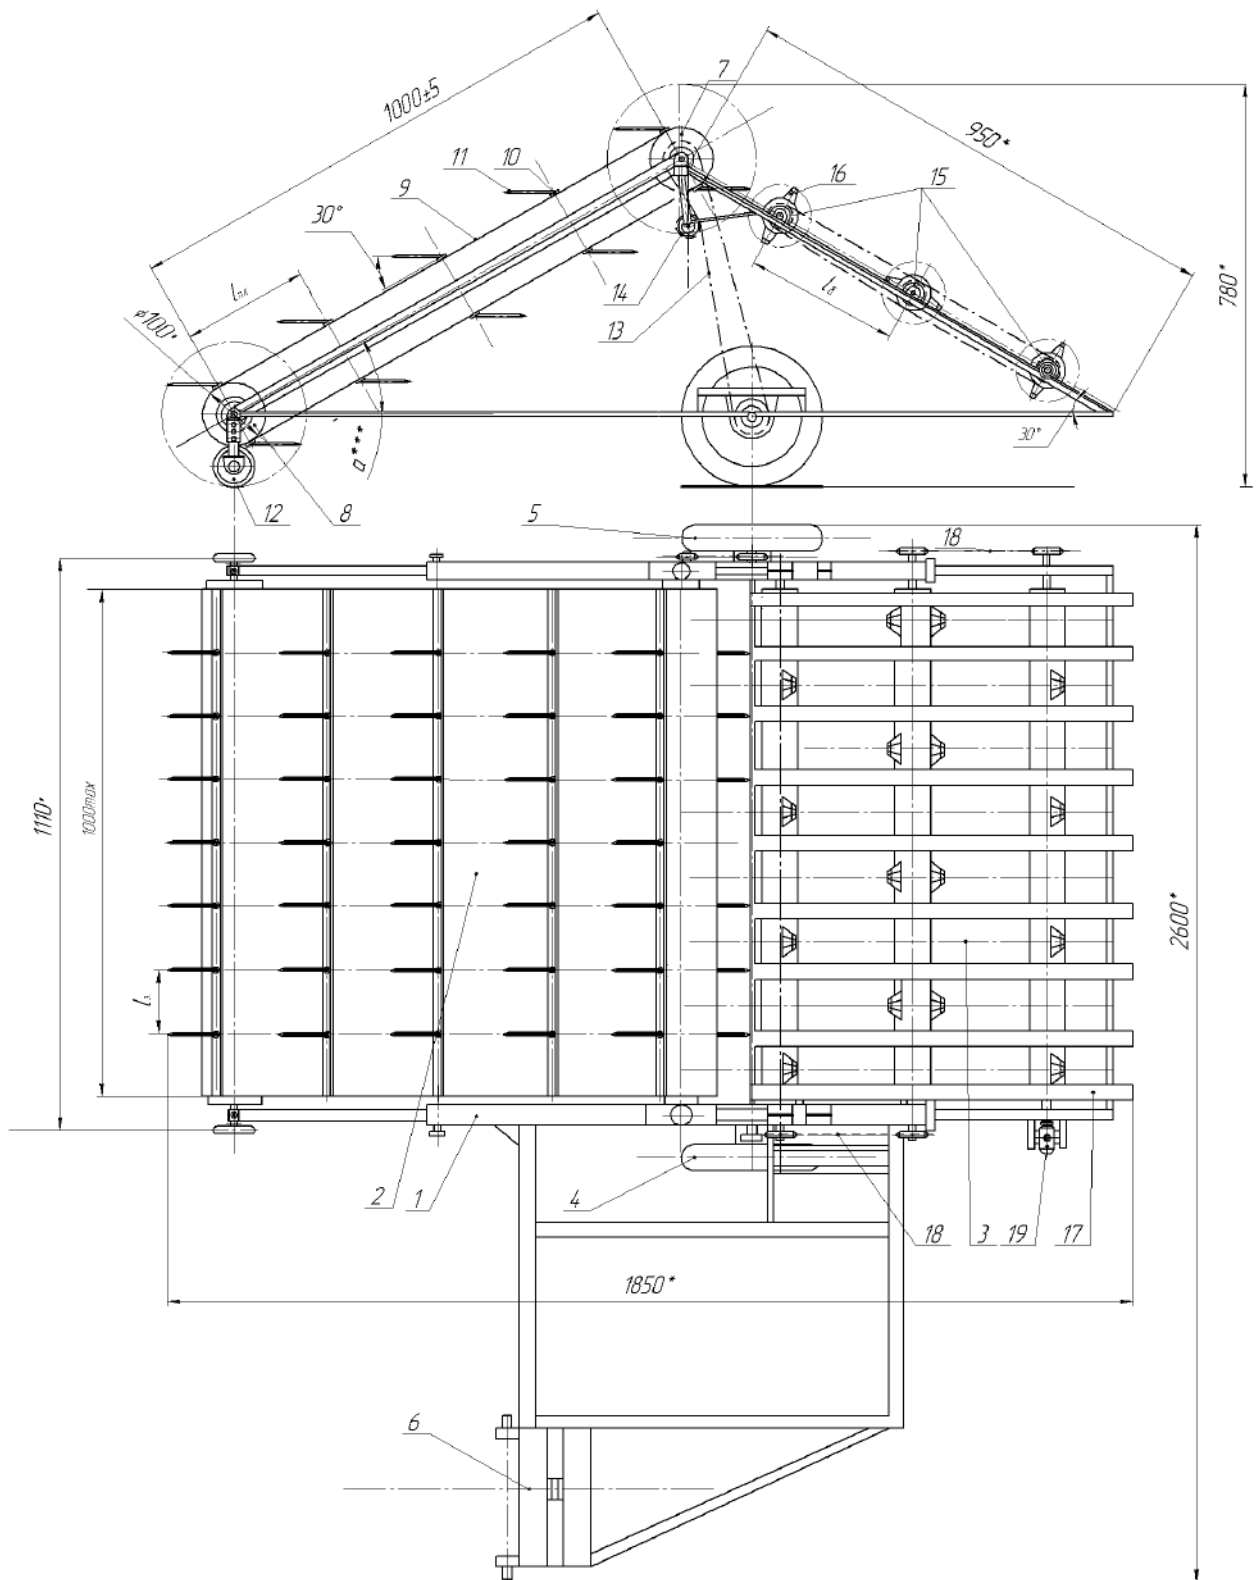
Конструктивно-компонувальна схема експериментального підбирача-розпушувача валків: 1 – рама; 2 – підбиральний вузол; 3 – розпушувальний вузол; 4,5,12 – колеса; 6 – навіска; 7,8 – барабани; 9 - стрічка; 10 – планка; 11 – зуб; 13,18 – ланцюг; 14 – зірочка; 15 – бітери; 16 – бітерний кулачок; 17 – решітка; 19 – електродвигун.
